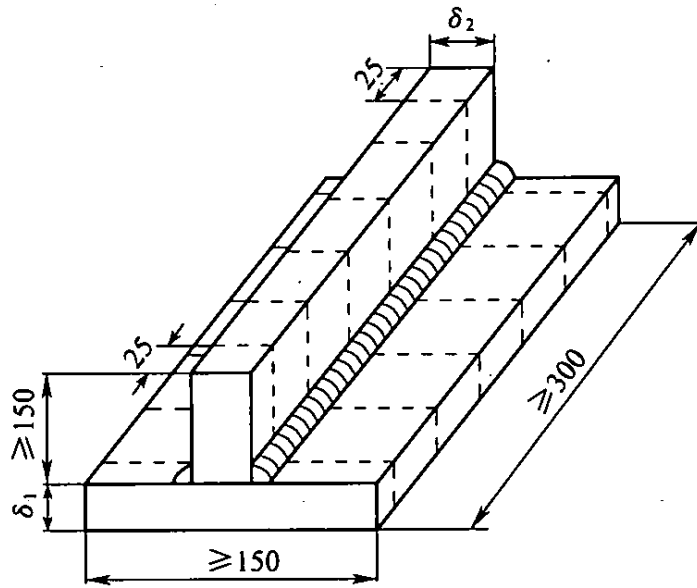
1 角焊缝试件及试样(mm)
